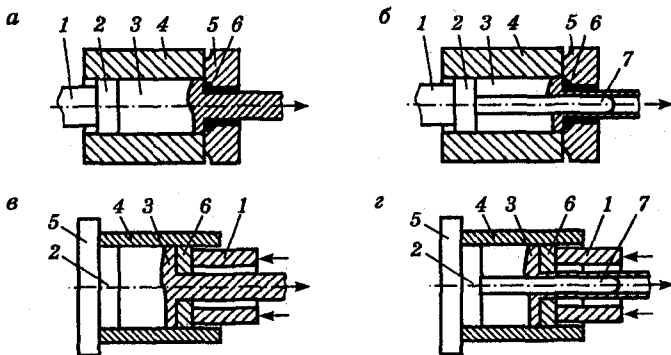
Схемы прямого прессования сплошного (а) и полого (б) профилей и обратного прессования сплошного (в) и полого (г) профилей
